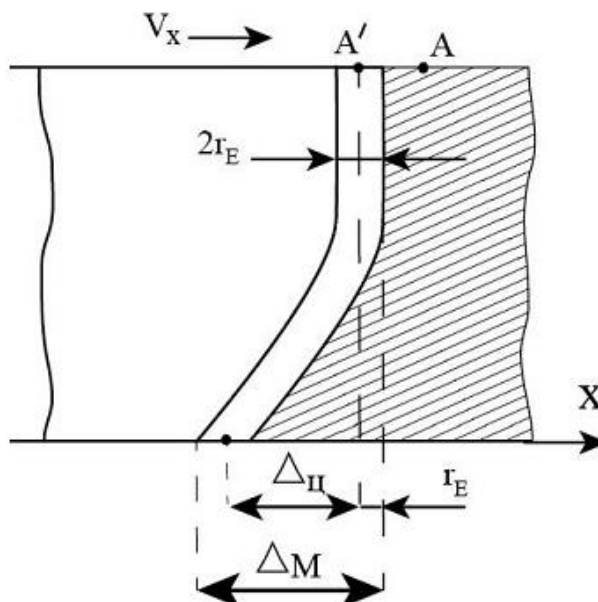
Схема поверхні невибраного матеріалу на нижній площині заготовки.
